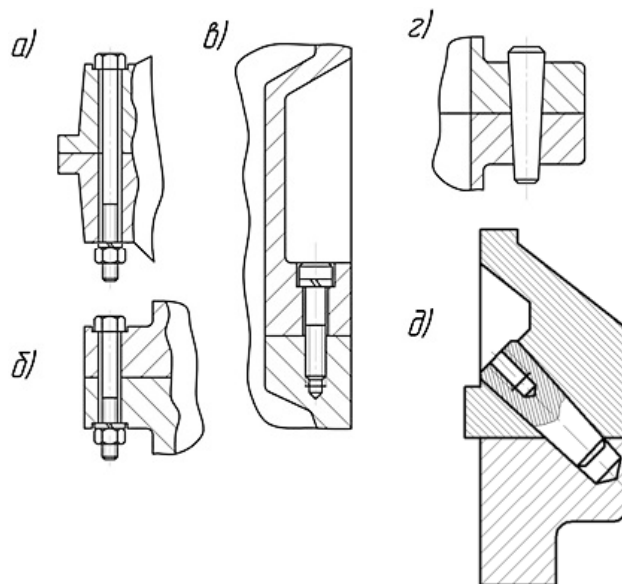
Приклади з'єднань кришки із корпусом редуктора
